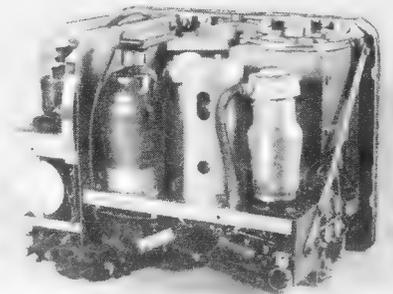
Der Chassisaufbau ist sorgfältig ausgeklügelt
